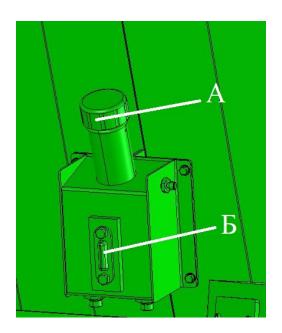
Бачок для смазки конических планетарных редукторов
